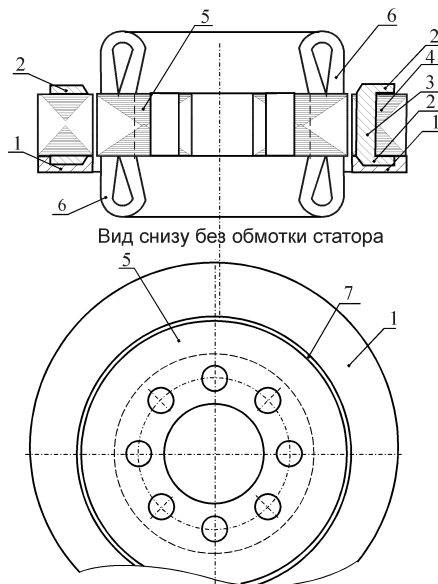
Схема конструкции электромагнитной части АМВ: 1 – ферромагнитный экран (наружный диаметр 460 мм), 2 – короткозамыкающие кольца обмотки ротора из алюминиевого сплава, 3 – стержни обмотки ротора, 4 – пакет ротора, 5 – пакет статора, 6 – лобовые вылеты обмотки статора, 7 – воздушный зазор между ротором и статором
